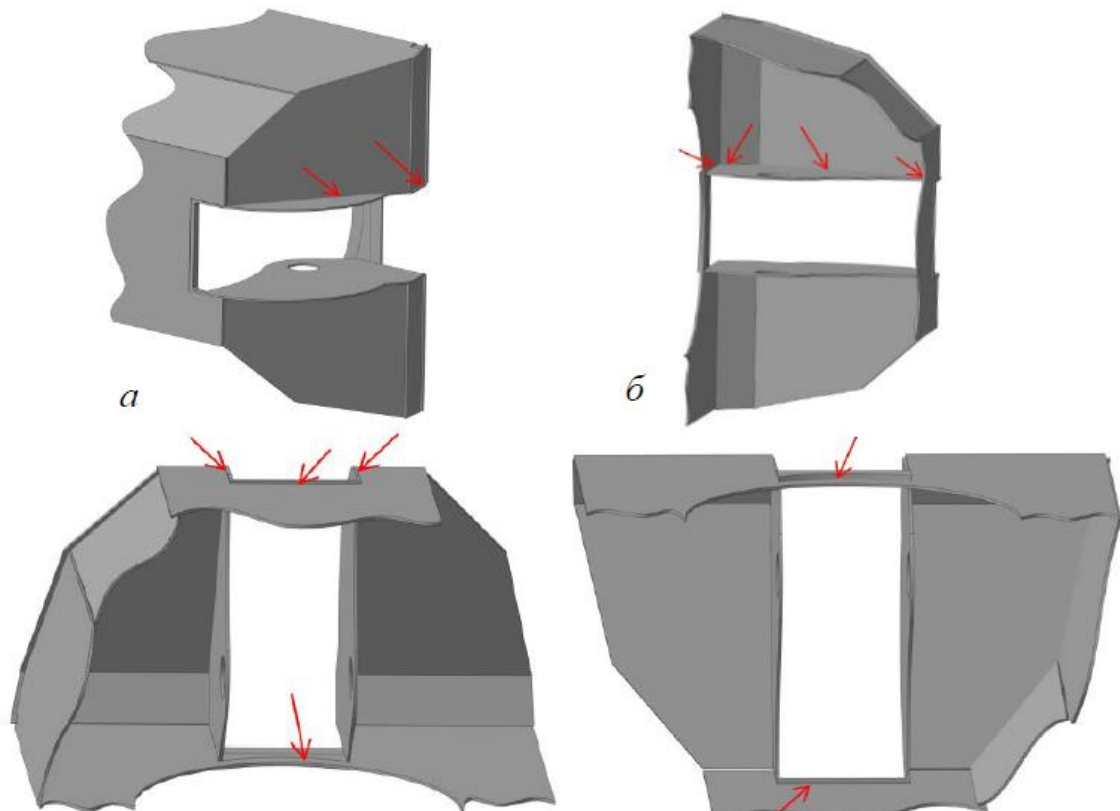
Положення корпусу при зварюванні (стрілочками показані зварні шви)
